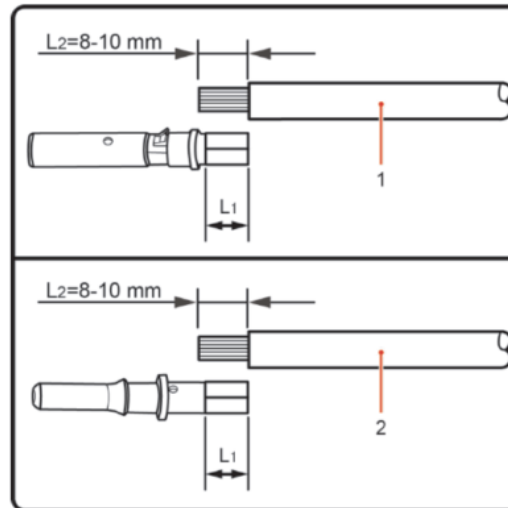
позитивний (1) і негативний (2) роз'єми MC4
